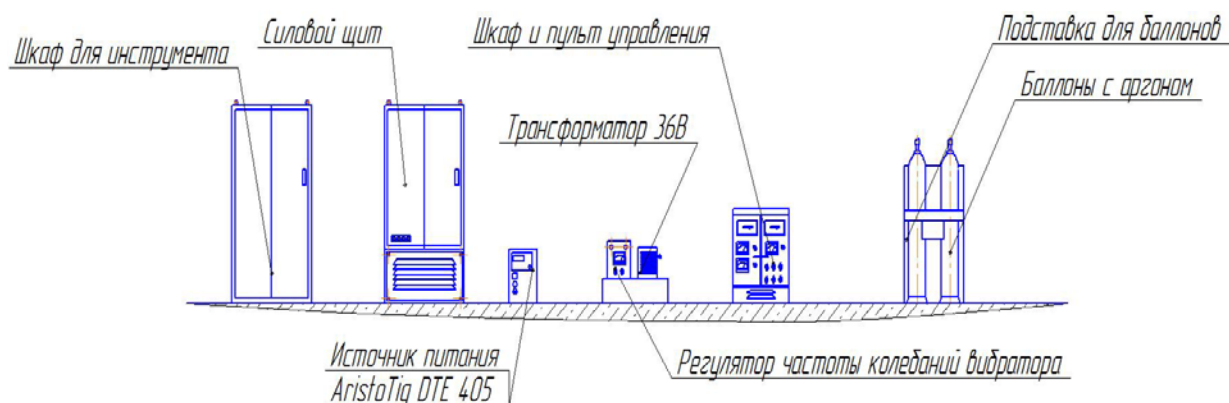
Установка для сборки и сварки (дополнительное оборудование)
